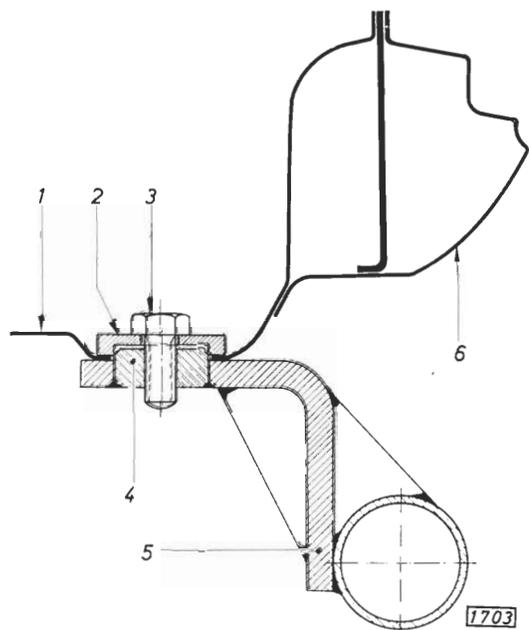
Schweißlehre an Bodenblech festgeschraubt – Bild zeigt einen von zwei Aufnahmeböcken
